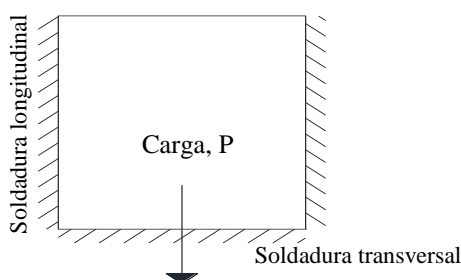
11 Soldadura de filete longitudinal y transversal
